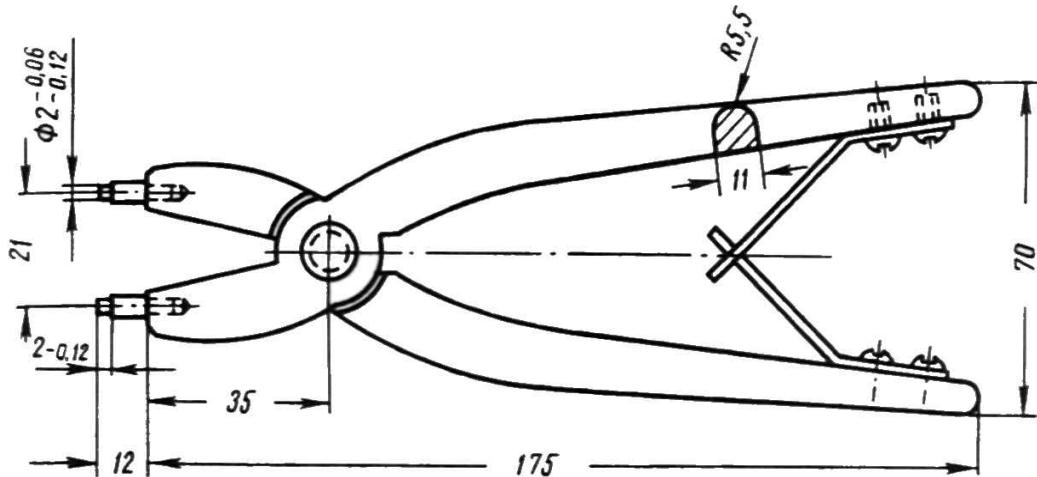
Щипцы для удаления и установки стопорных колец
